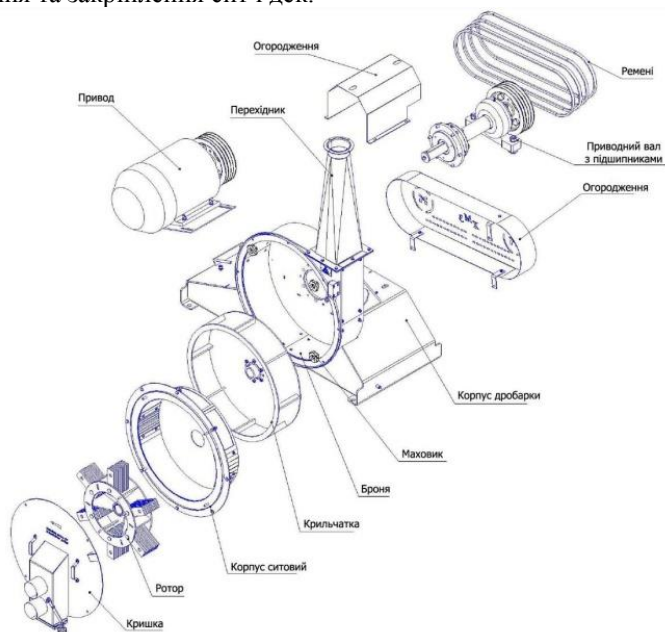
Конструкційна схема дробарки ДМП-22
